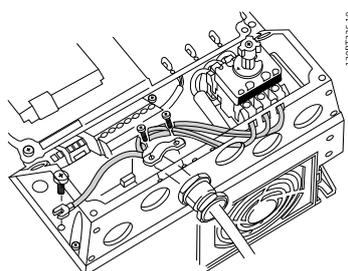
Connexion au secteur et à la terre avec sectionneur secteur.
